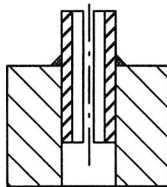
Prinzipskizze zur Aufgabe "Laserschweißen einer Hülse"
